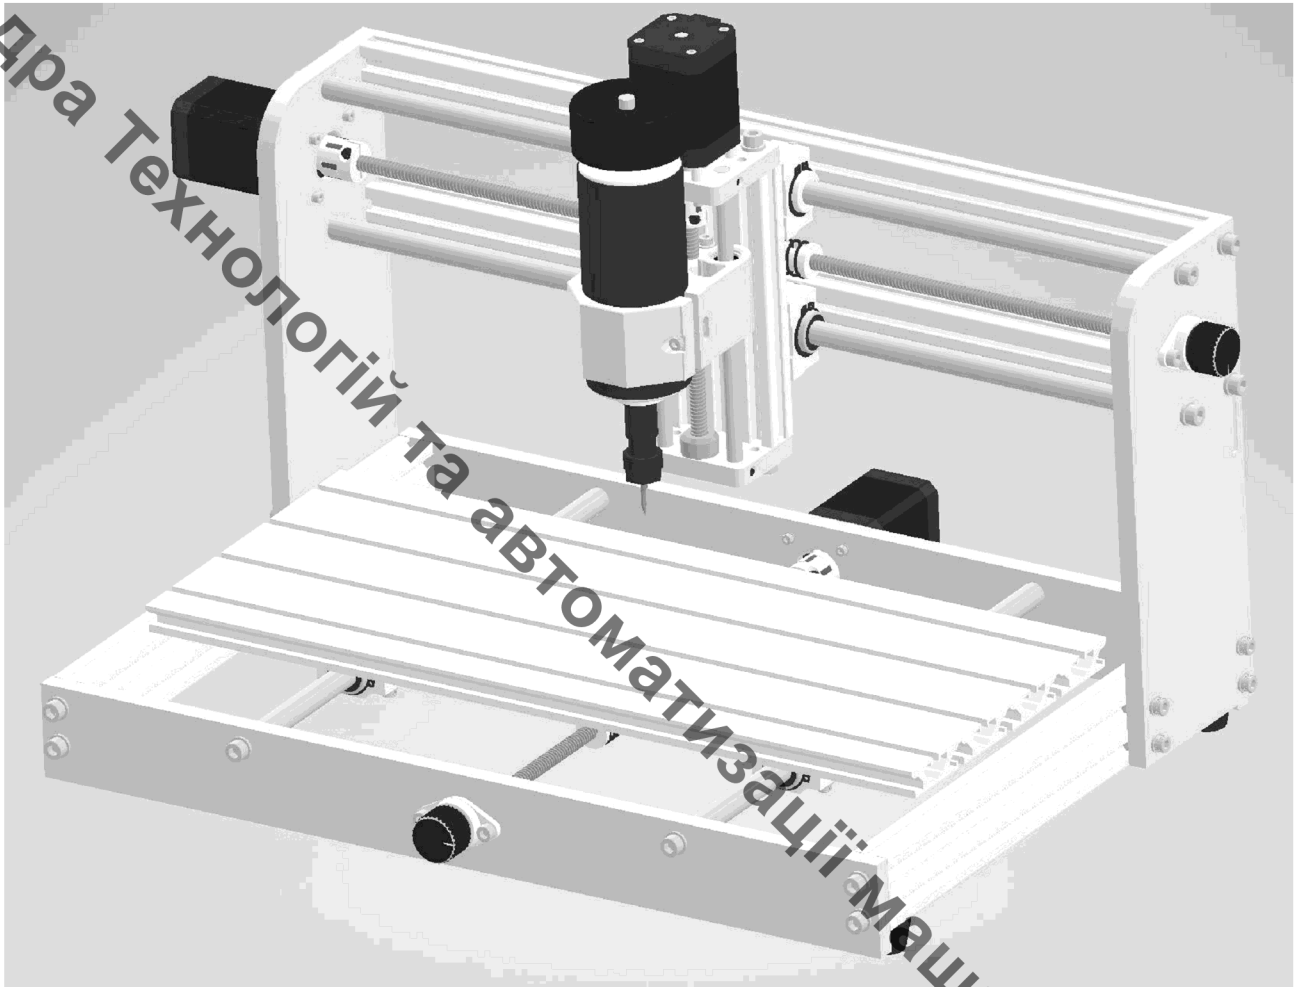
Несуча конструкція фрезерно-гравірувального верстата з ЧПК разом з основними вузлами
